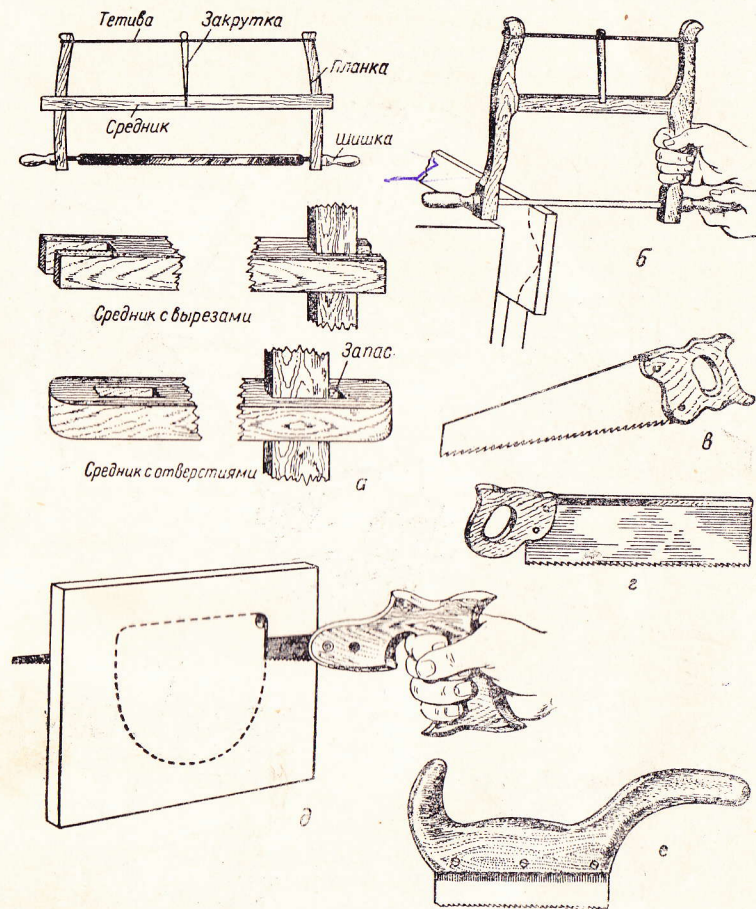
Пилы: а — лучковая пила и ее части; б — выкружная лучковая пила; в — широкая ножовка; г — ножовка с обушком; д — узкая ножовка; е — наградочная ножовка.
